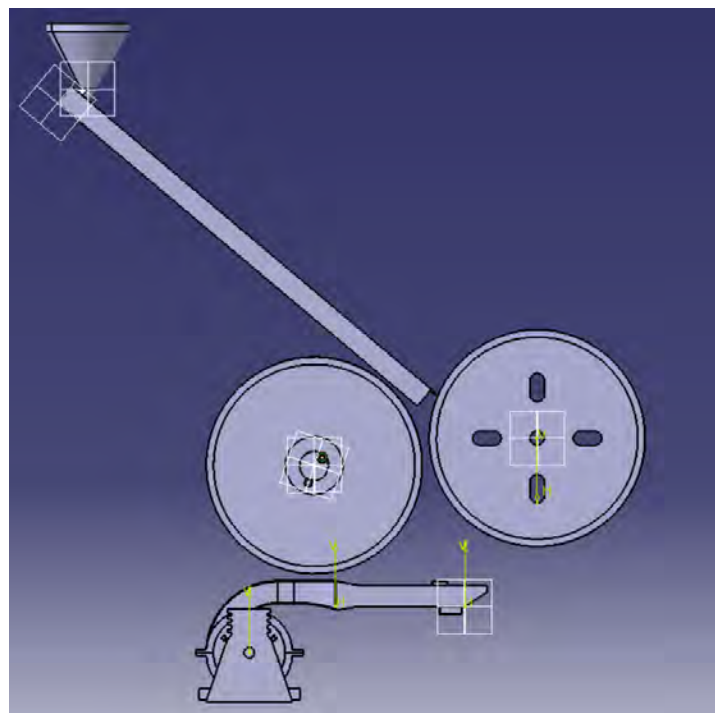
Vista lateral del ensamble de la máquina de descascarado (realizado en Catia V5)
